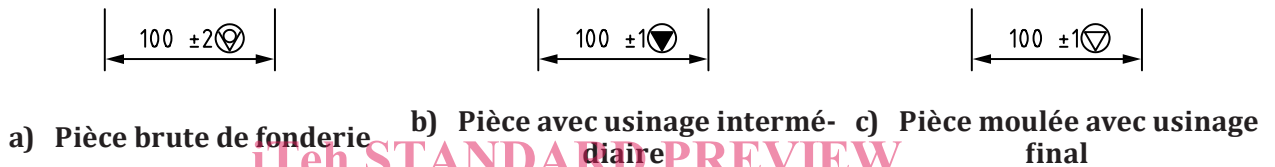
Exemples de dimensions nominales avec tolérances particulières
